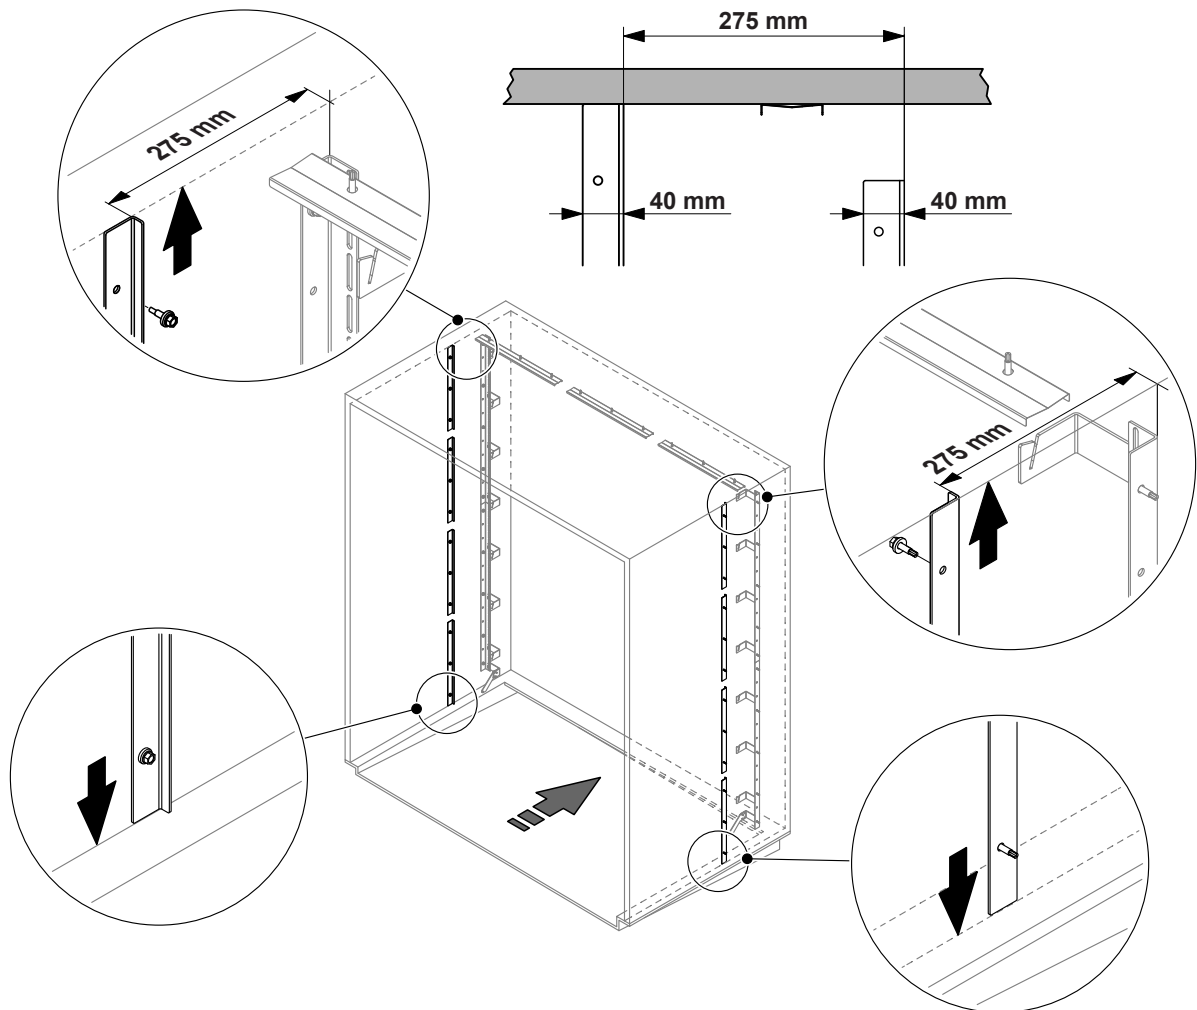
Montaje de los perfiles de fijación de las chapas de cierre laterales
